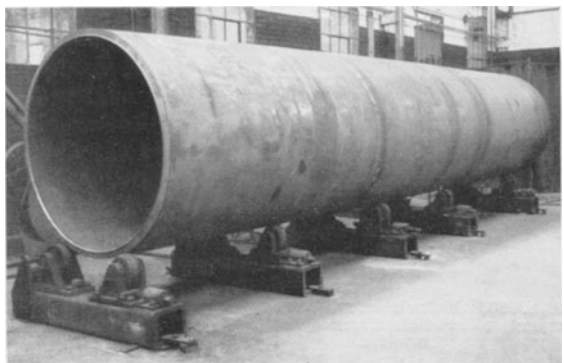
Geschweißter Hochdruckkesselmantel auf Rollböcken.
